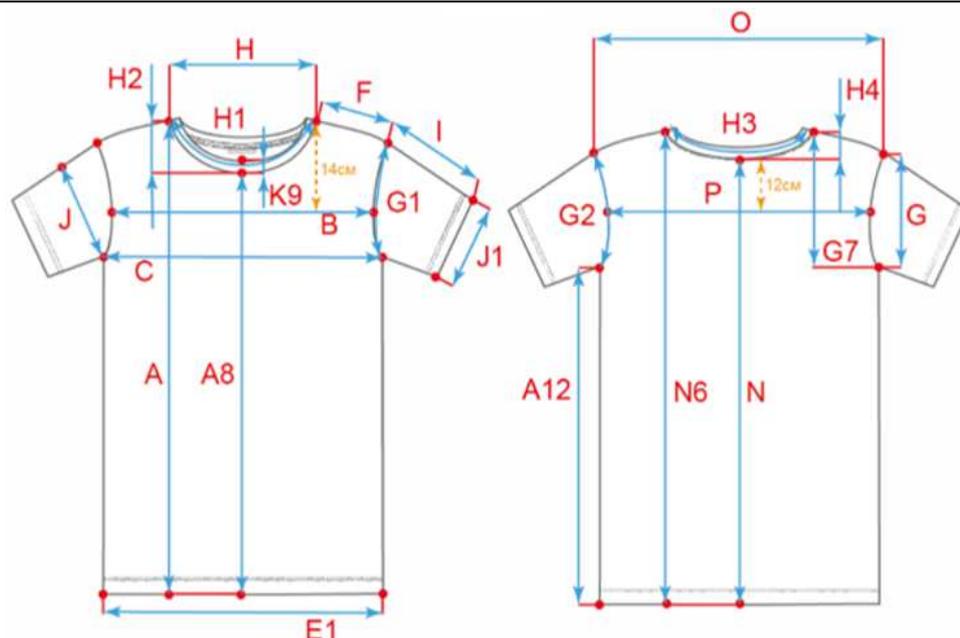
Схема параметризации футболки для контроля габаритов с помощью ПАК GarmentScanner
